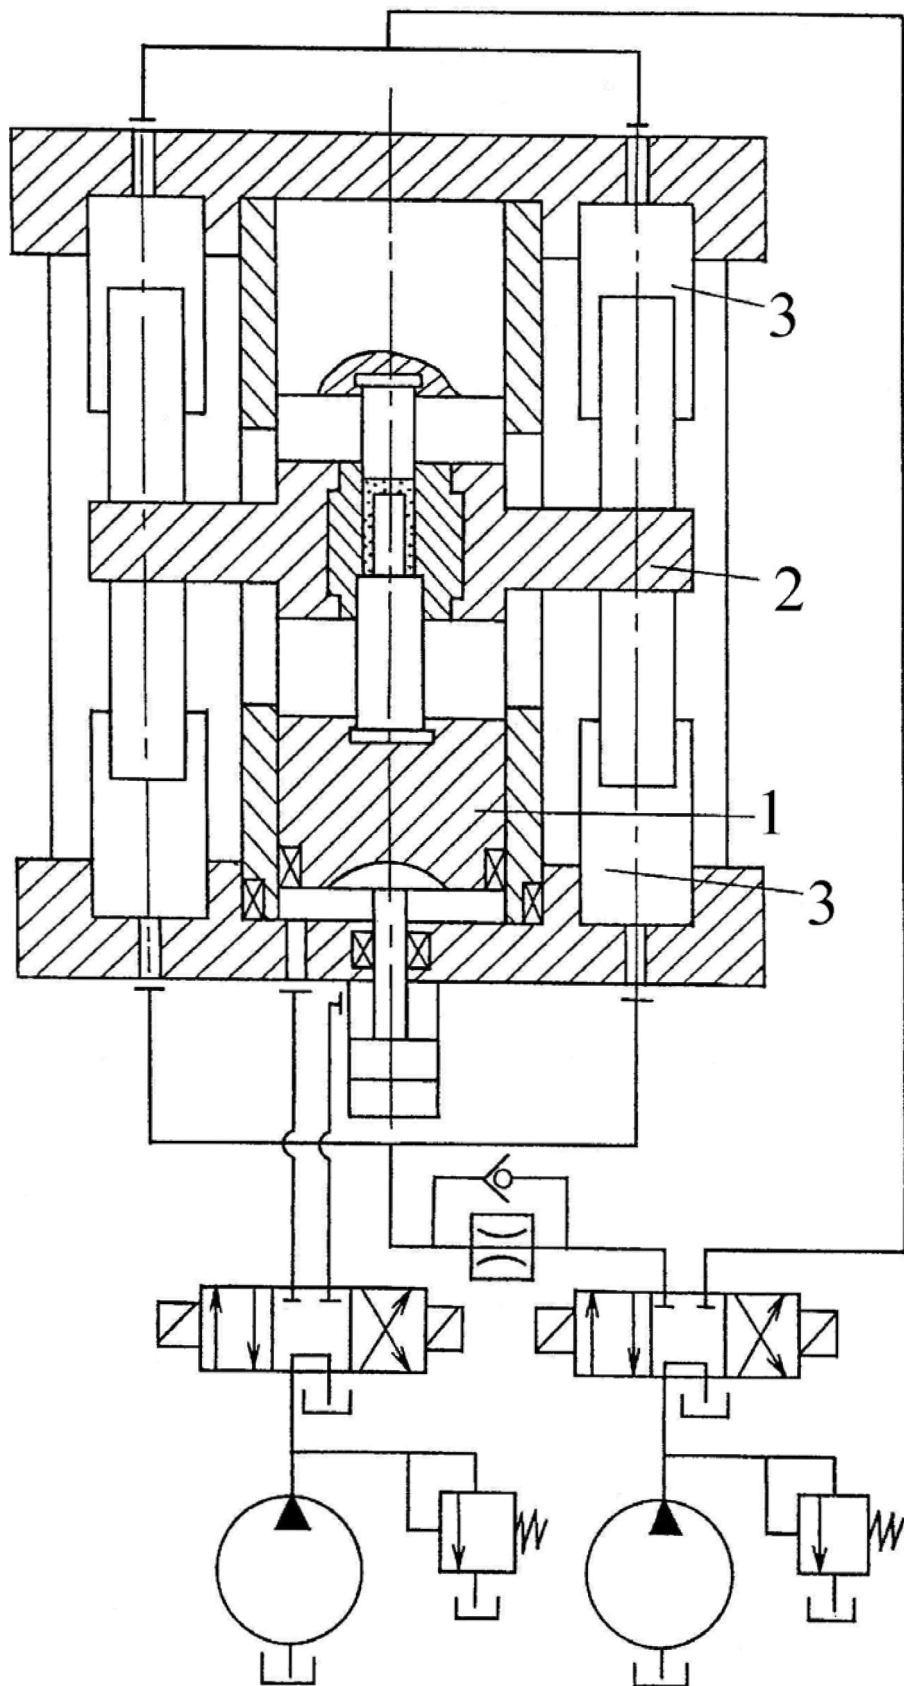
Конструкция пресса для выдавливания с активными силами трения
